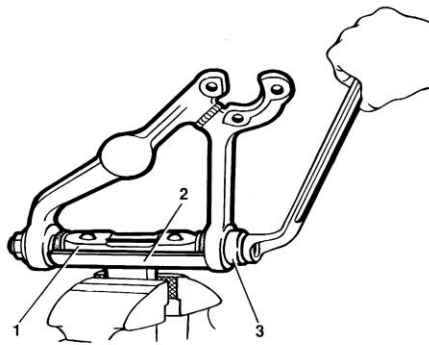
Запресовування шарнірів верхнього важеля
